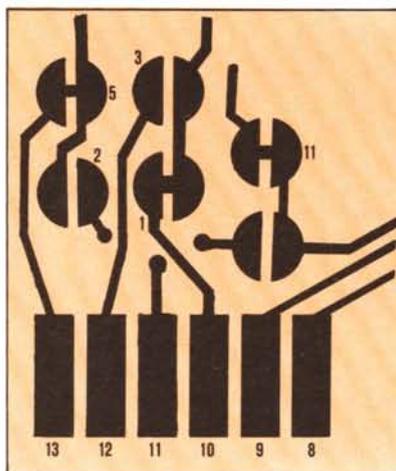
Particolare della espansione 3K RAM prima di correggere i pallini.
